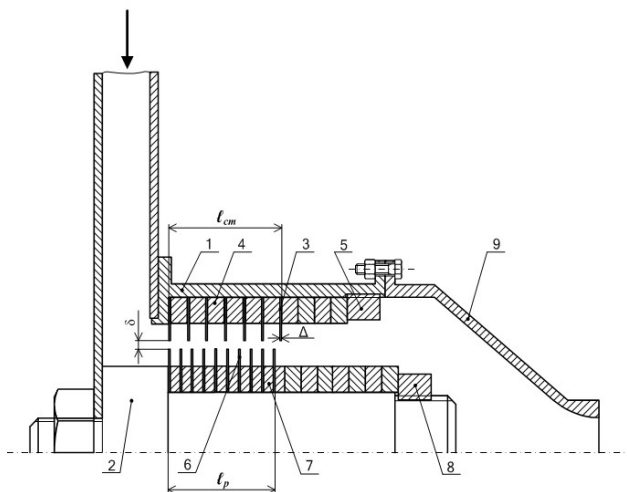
Конструктивная схема установки для исследования РМУ: 1 – корпус; 2 – ось; 3 – гребешок статора; 4 – проставка статора; 5 – гайка; 6 – гребешок ротора; 7 – проставка ротора; 8 – гайка; 9 – сопло
